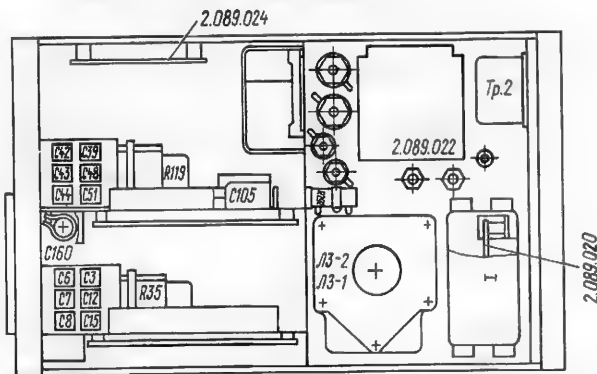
Схема расположения установочных элементов и печатных плат (вид снизу):
